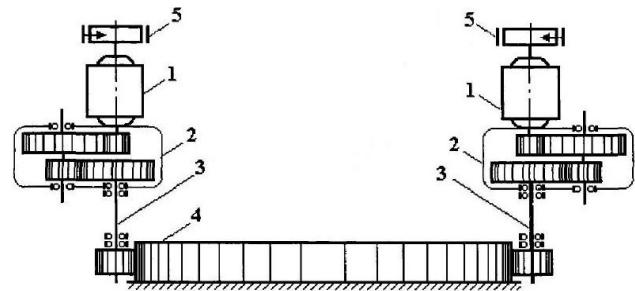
Кинематическая схема механизма поворота экскаватора
